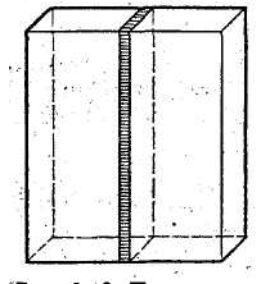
Приклад шва при електрошлаковому зварюванні
